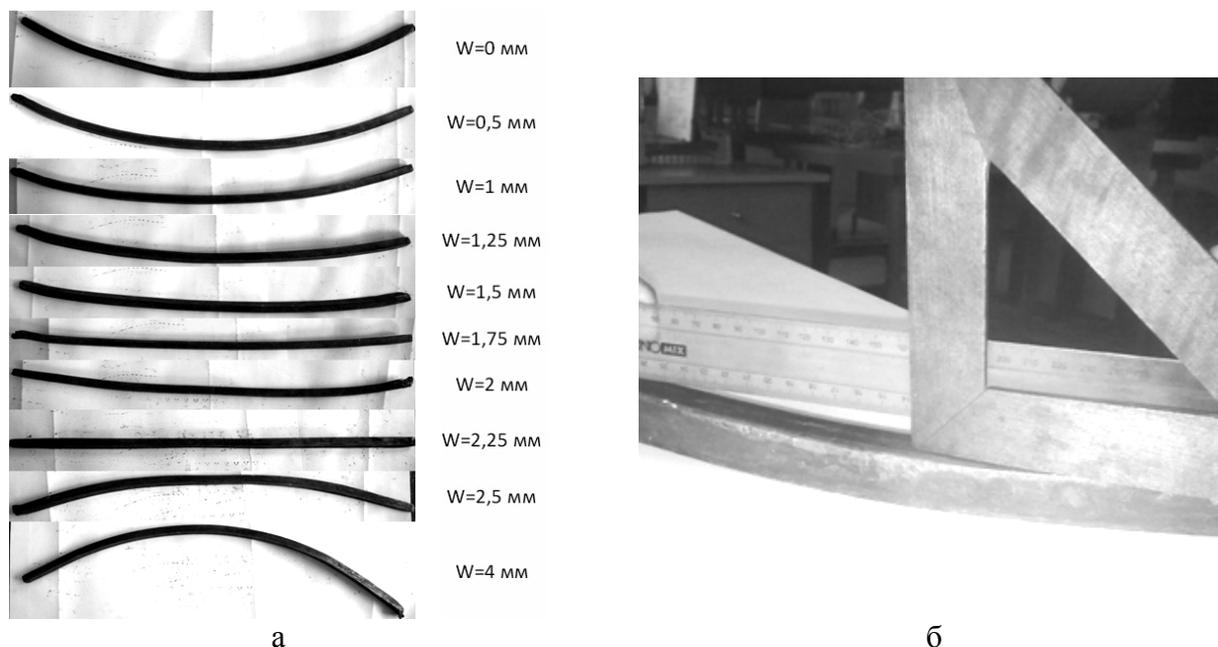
Общий вид заготовок после правки (а) и методика измерения кривизны заготовки (б)
